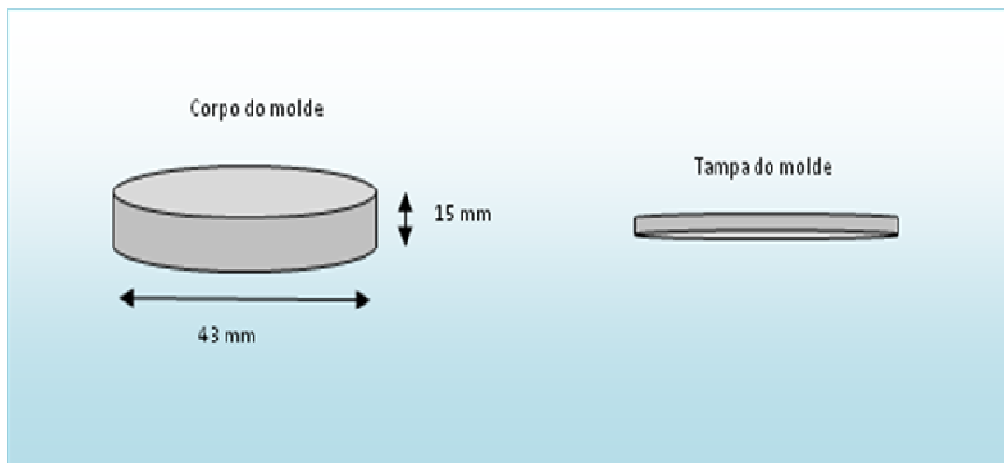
Molde utilizado para a fabricação dos meios filtrantes.
